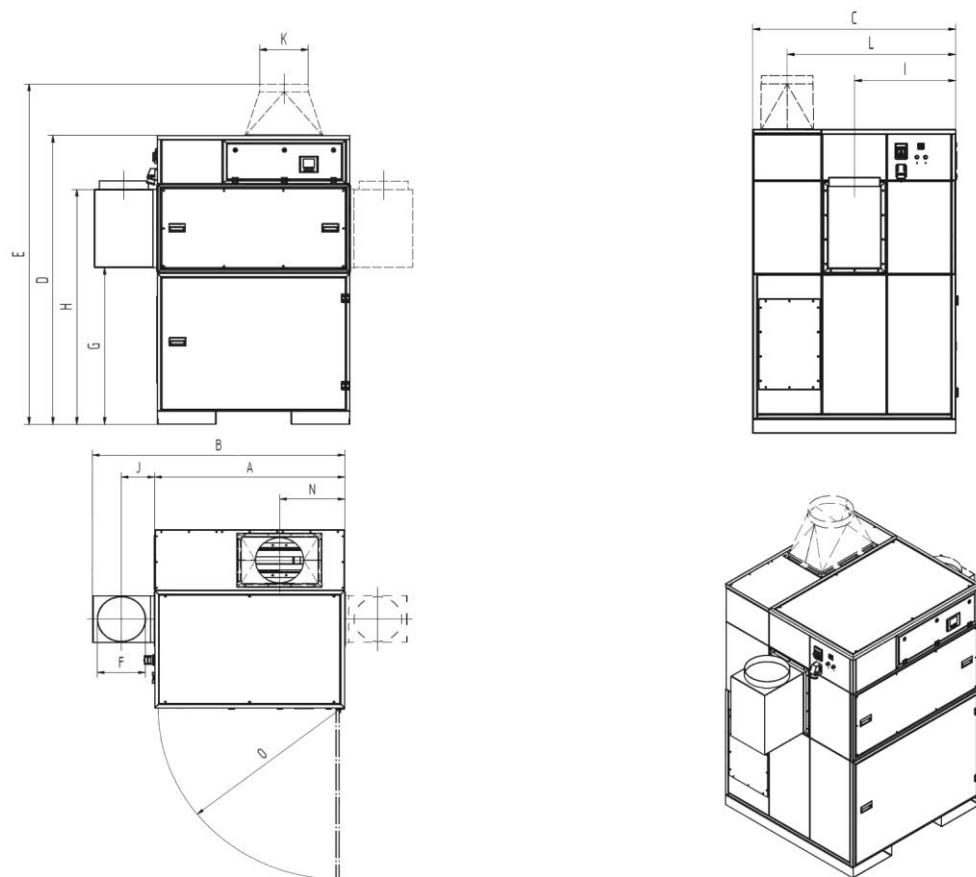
Габаритный чертеж 3540, 3730, 323015, 323016
